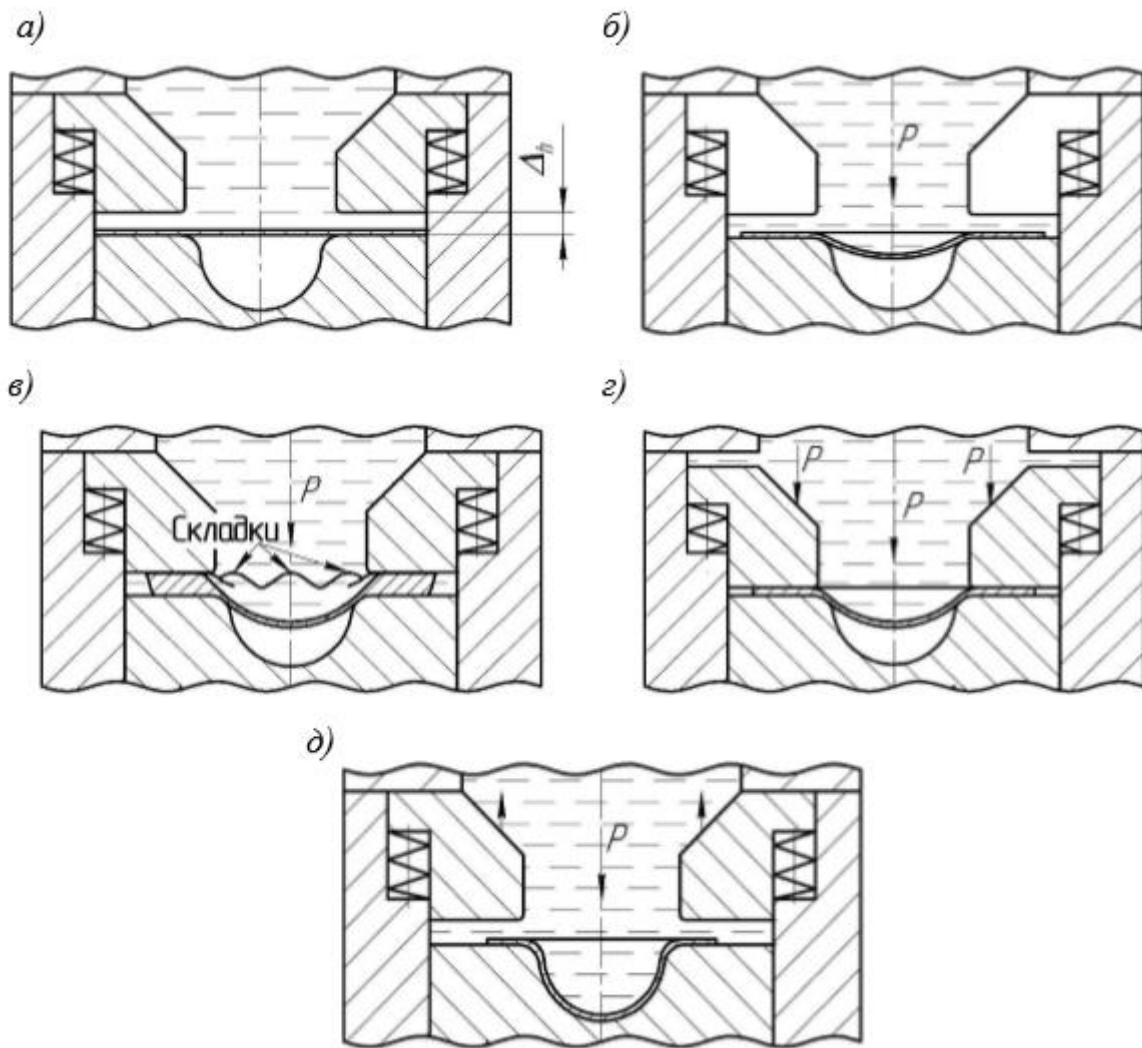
Етапи формозміни за пропонованою інтенсифікованою схемою: а – вихідне положення заготовки та оснащення; б – формозміна центральної частини заготовки; в – утворення складок на фланцевій частині заготовки, порушення течії металу; г – рух інерційного розгладжувача та розгладжування гофрів на фланці; д – додаткова формозміна заготовки без опору гофрів
